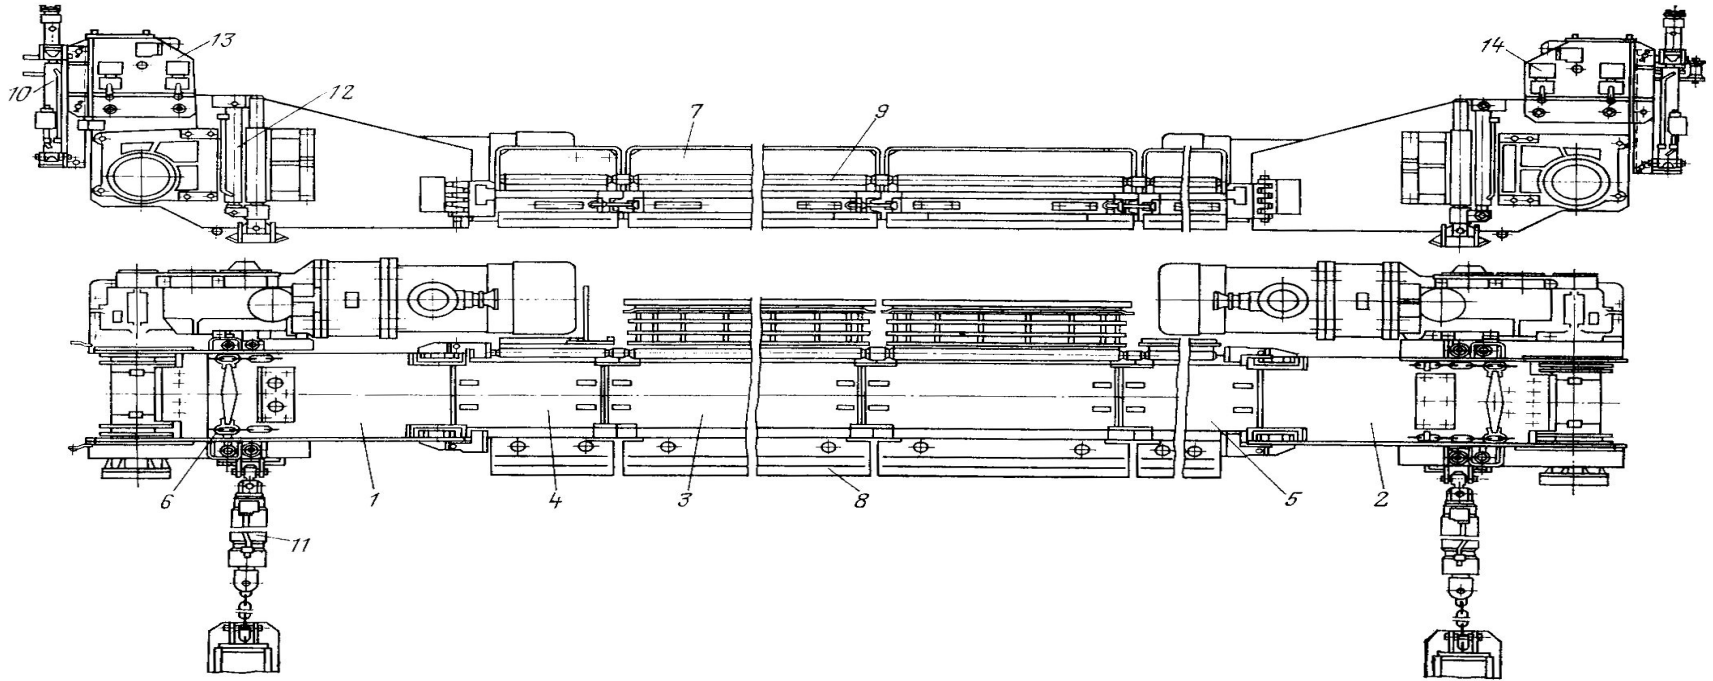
Скребковый передвижной забойный конвейер СП-202: 1-концевая головка; 2-линейные рештачный став; 3-тяговый орган (цепь со скребками); 4-головной привод
